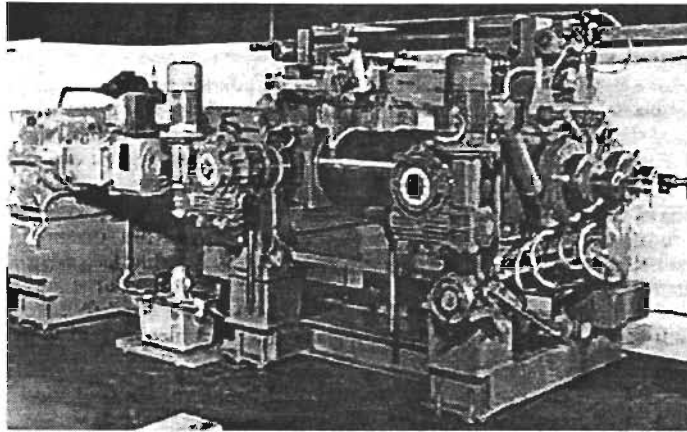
Molino de rodillos. Foto de catálogo, www.santoshrubbermachinery.com
